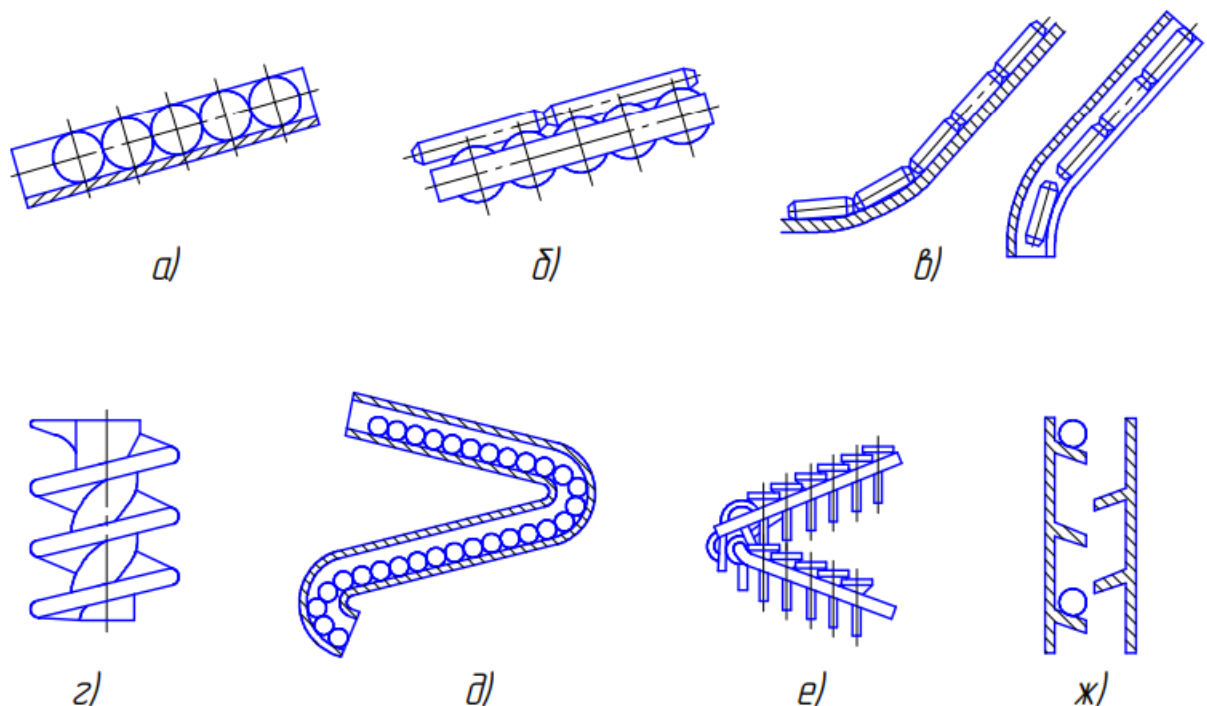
Схеми магазинних допоміжних пристроїв типу лотки
